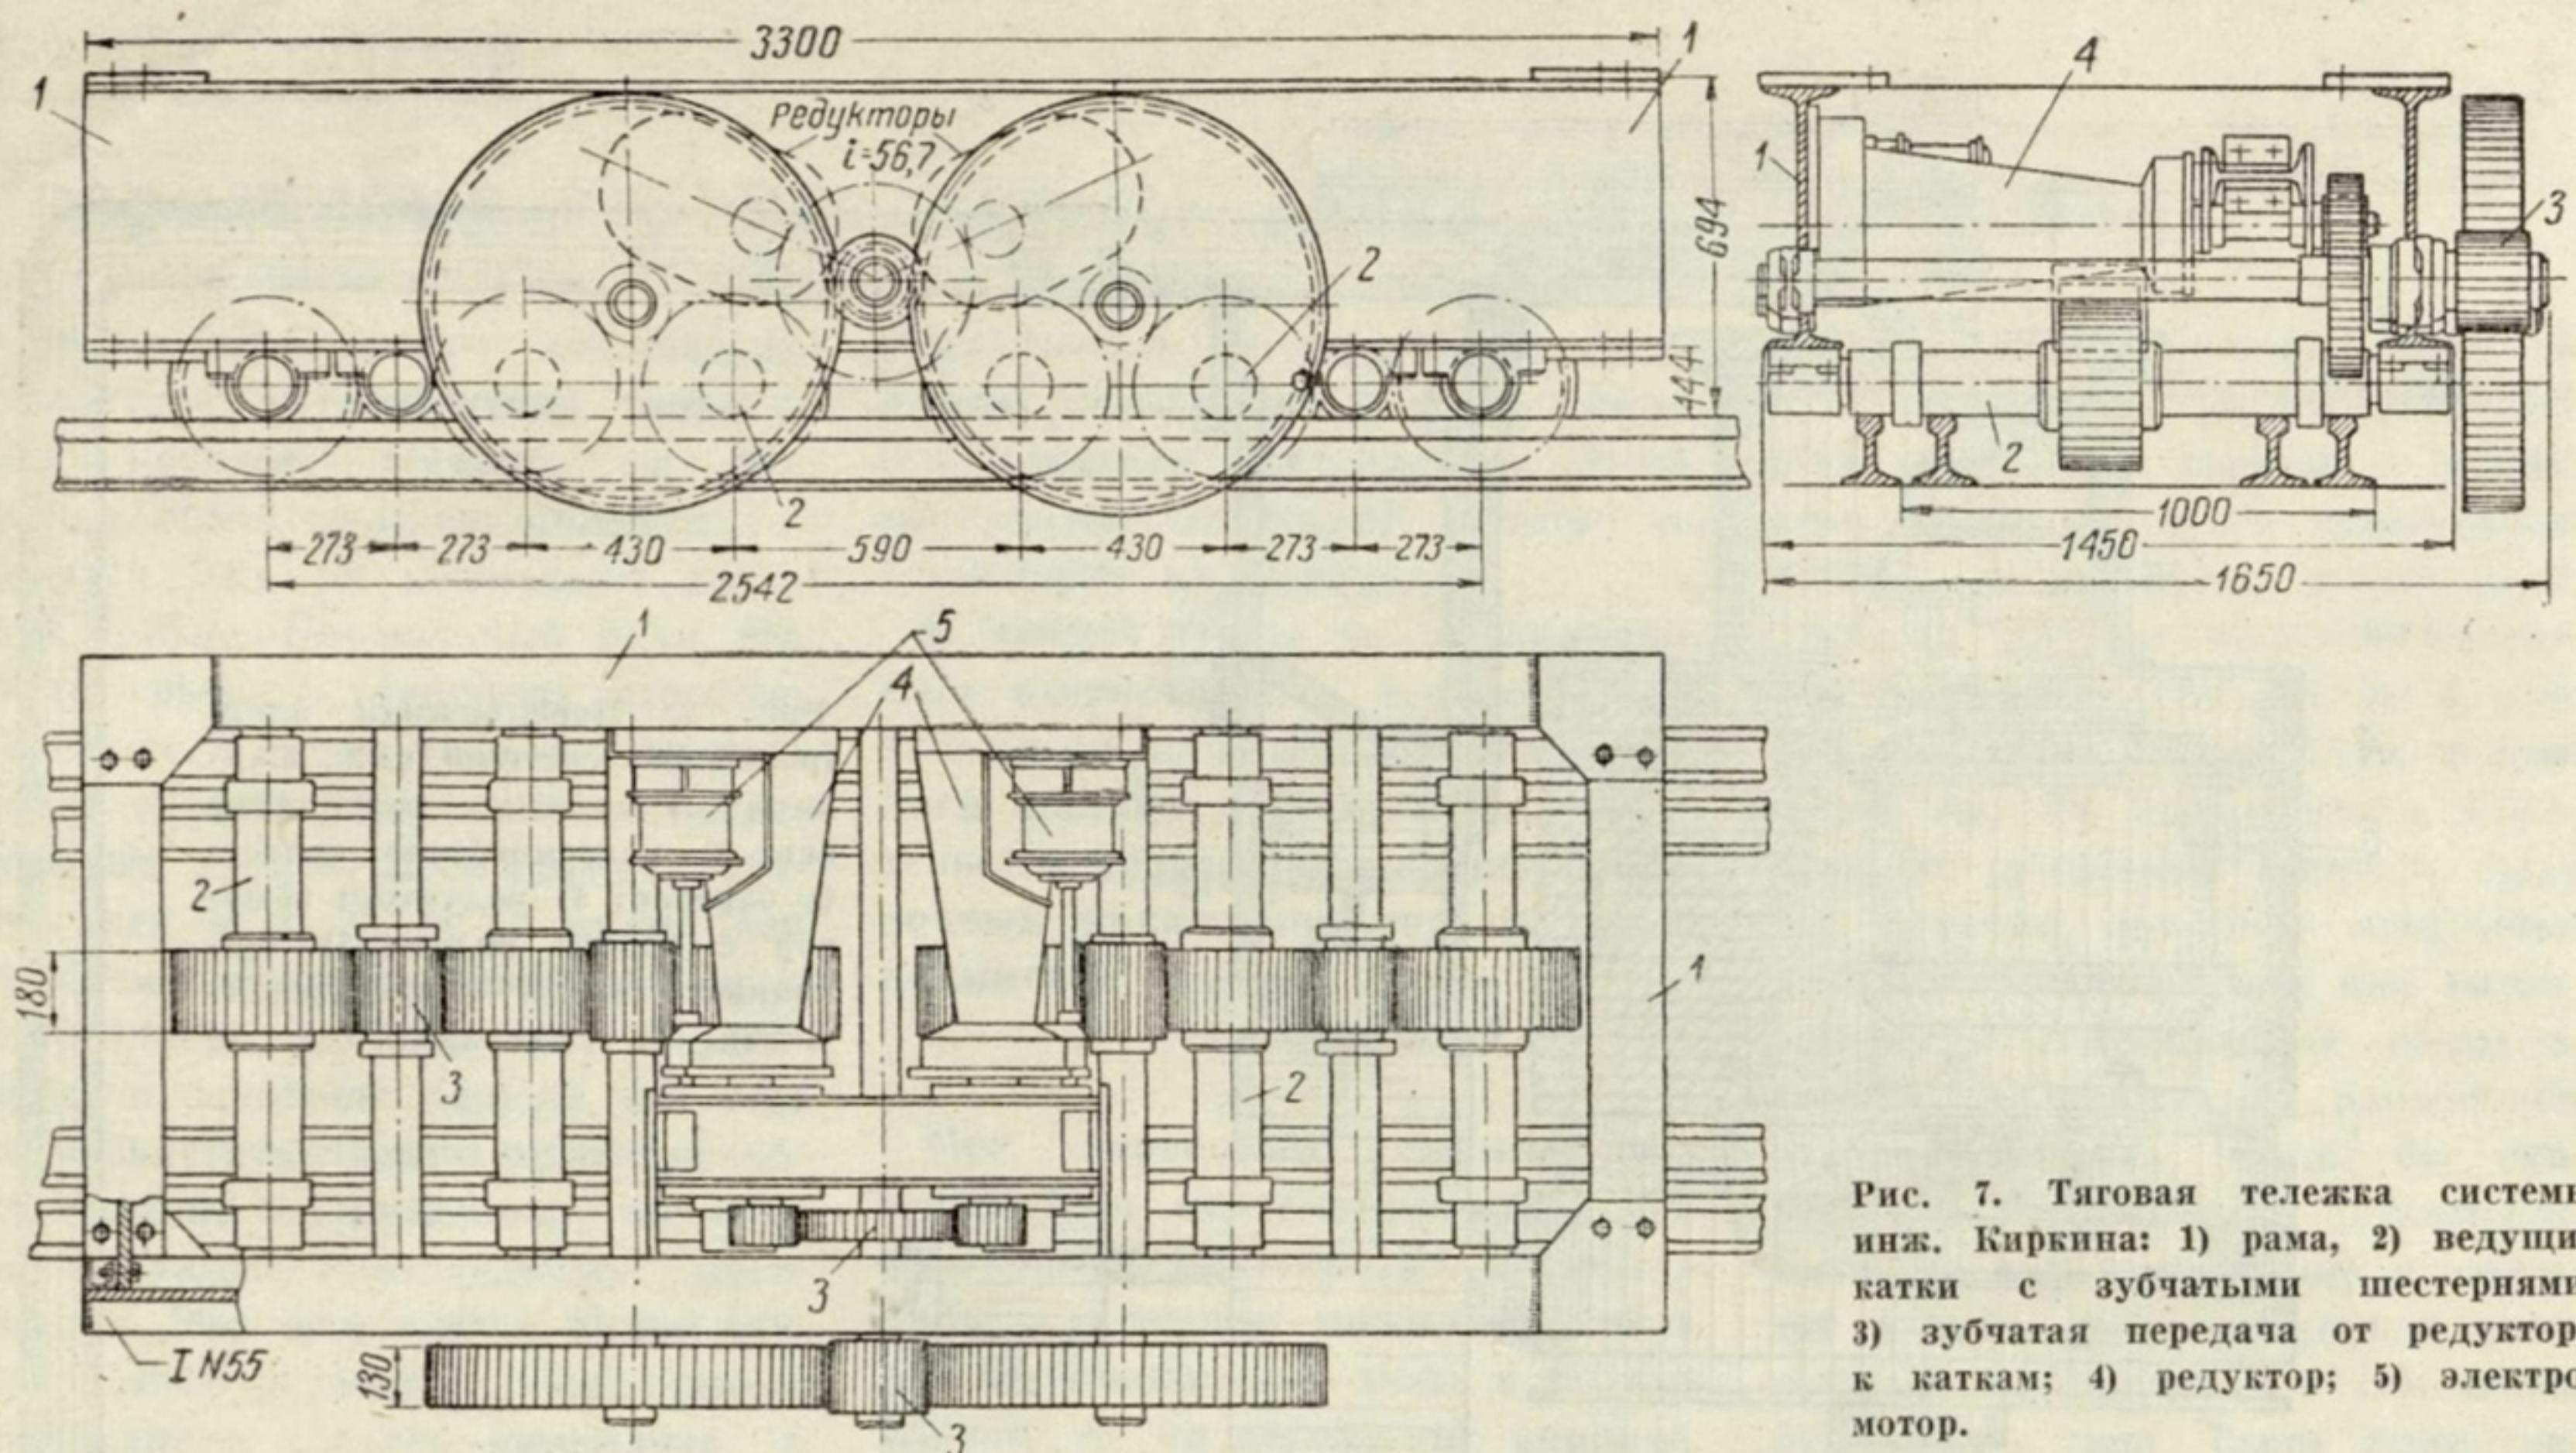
Тяговая тележка системы инж. Киркина: 1) рама; 2) ведущие катки с зубчатыми шестернями; 3) зубчатая передача от редуктора к каткам; 4) редуктор; 5) электромотор.
